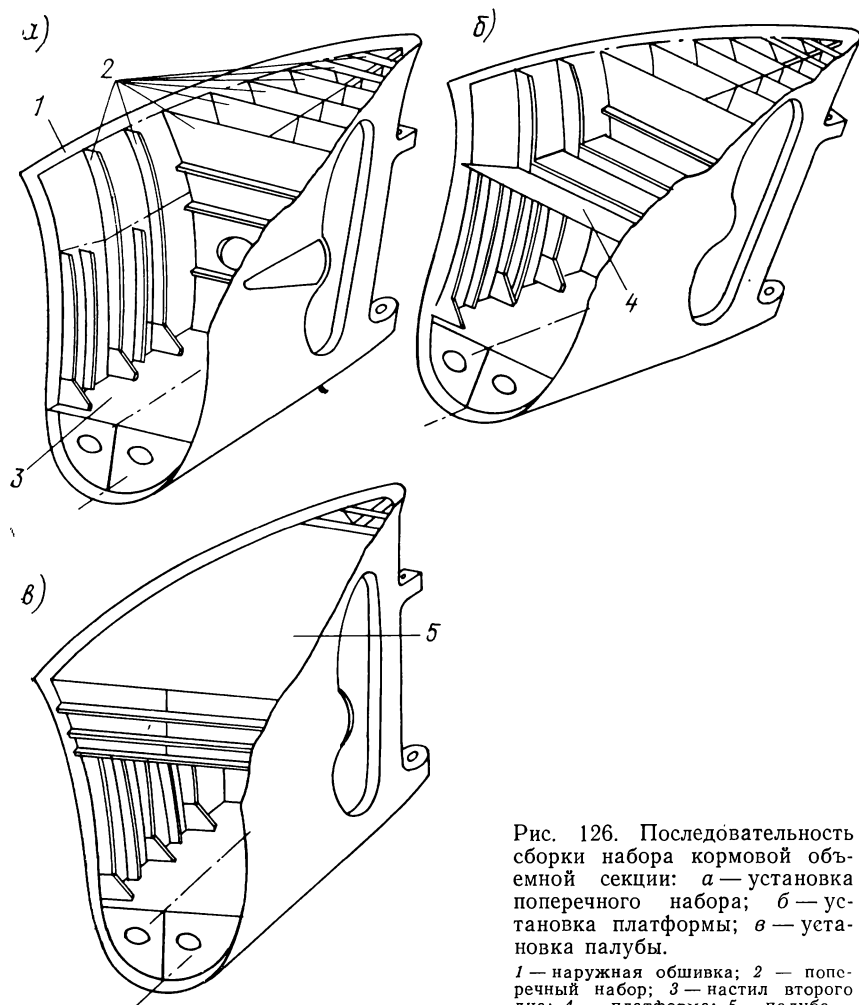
Последовательность сборки набора кормовой объемной секции: *а* — установка поперечного набора; *б* — установка платформы; *в* — установка палубы.
